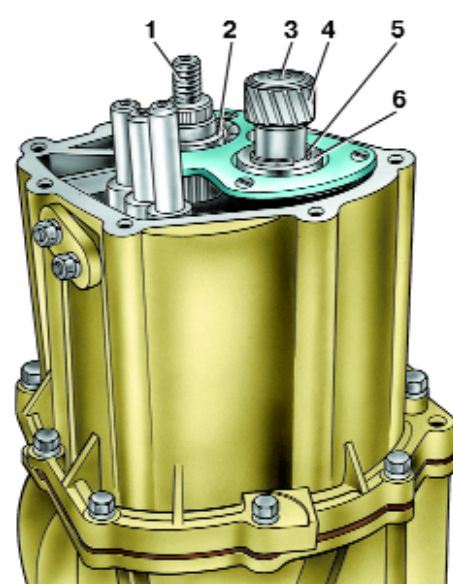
Установка на валы втулок и колец, примыкающих к шестерням пятой передачи: 1 – вал ведущей шестерни главной передачи; 2 – заднее внутреннее кольцо заднего подшипника ведущей шестерни; 3 – первичный вал; 4 – втулка шестерни пятой передачи; 5 – упорное кольцо шестерни пятой передачи; 6 – шайба
